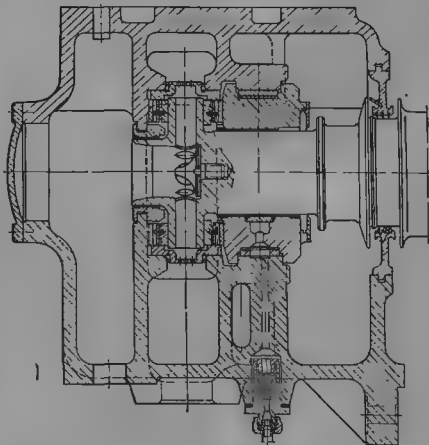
Комбинированный опорно-упорный подшипник и регулятор скорости.
